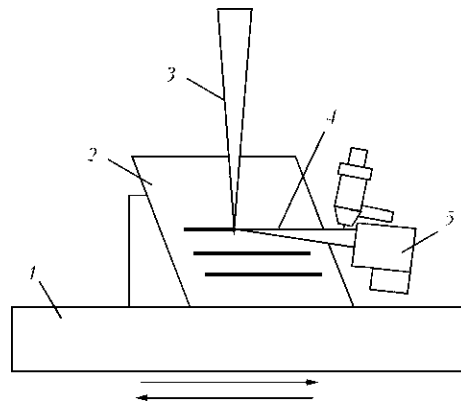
Схема процесса комбинированной лазерно-микроплазменной наплавки: 1 — станина; 2 — образец; 3 — лазерный пучок; 4 — плазменная струя; 5 — микроплазматрон
